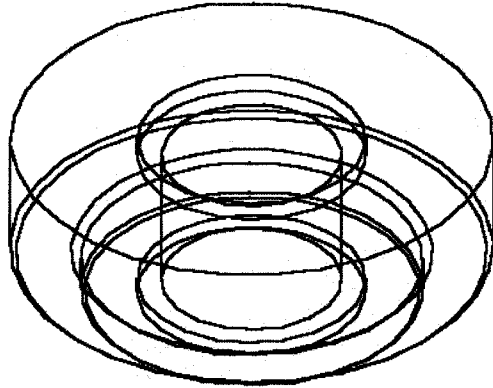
Axis-symmetry workpiece for Chuck Body C2
